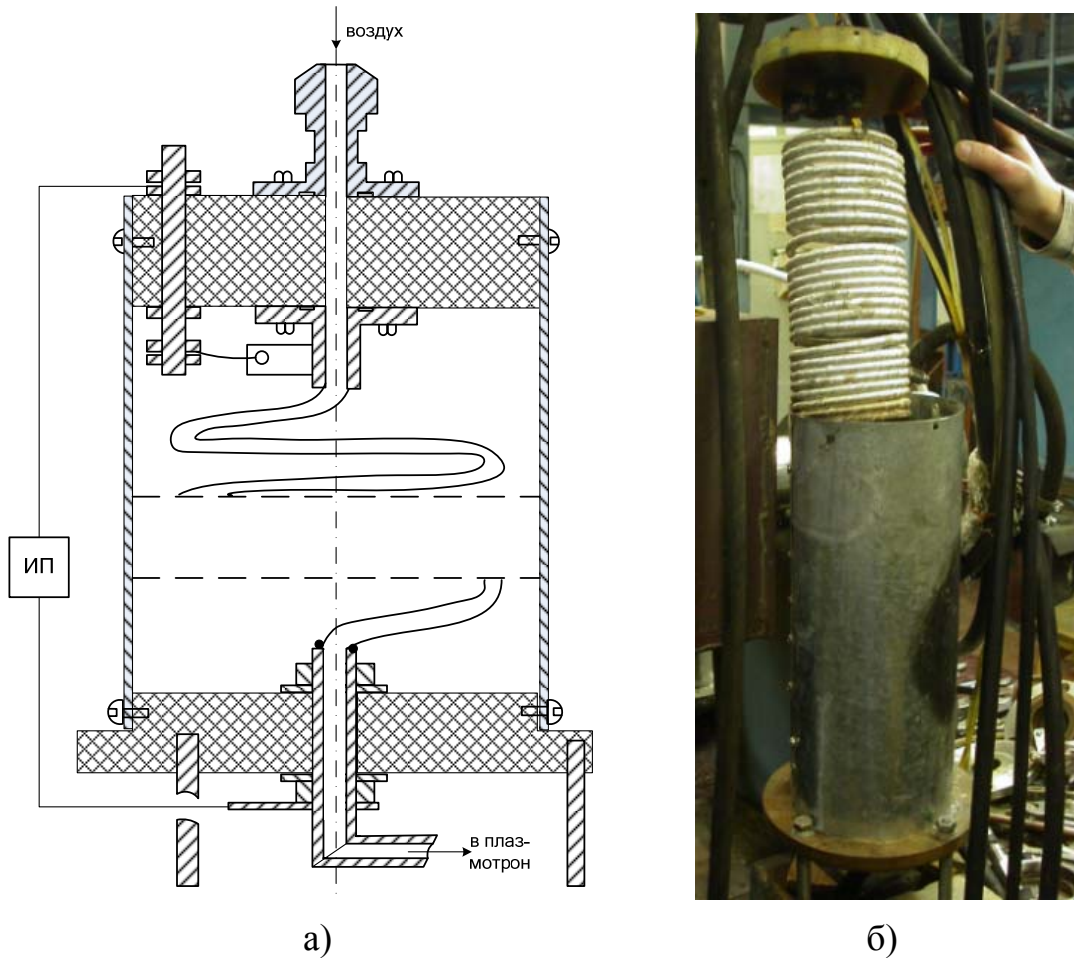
Нагреватель воздуха: а) конструктивная схема; б) фотография
